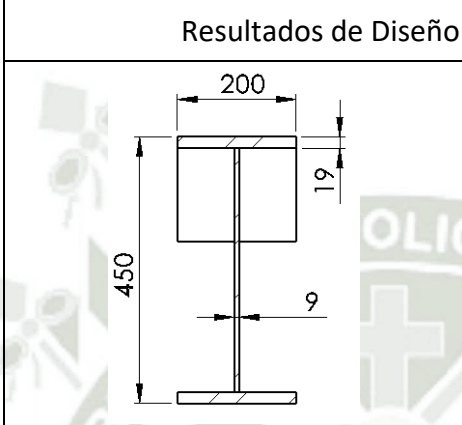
Representación de soldadura en Viga Principal
